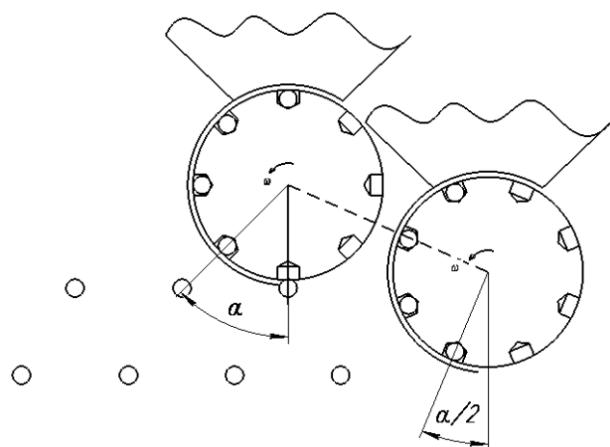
Схема работы tandemных дисковых высевающих аппаратов для осуществления двухстрочного посева
